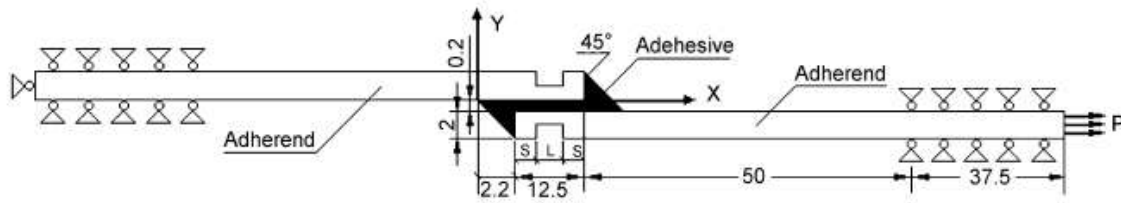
Geometria de junta de sobreposição simples com ranhuras paralelas nos aderentes [60].
